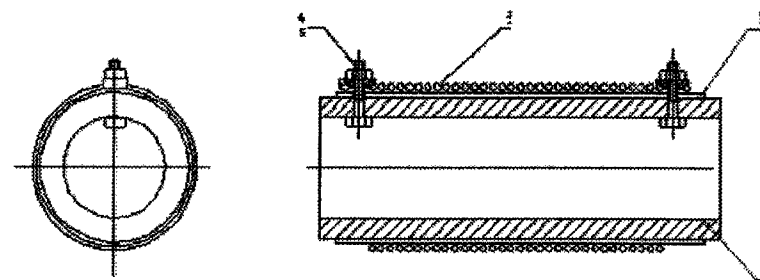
Эскиз заготовки: 1- молибденовая труба; 2- металлическая фольга; 3 - молибденовая проволока, 4,5 - стяжные элементы
